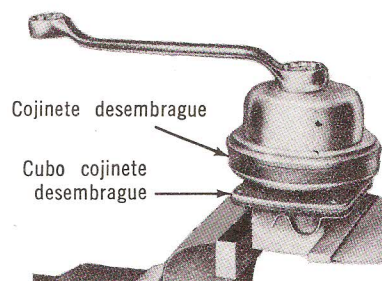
Instalando el Cojinete de Desembrague. 8 Cilindros.
